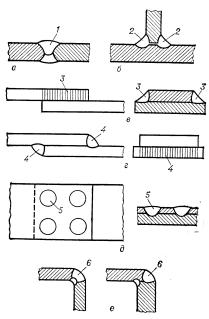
Виды сварных соединений и типы швов при дуговой сварке : a — стыковое; 6 — тавровое; e , z, ∂ — нахлёсточные; e — угловое; 1 — стыковой шов; 2 — угловой шов таврового соединения; 3 — фланговый угловой шов нахлёсточного соединения; 4 — лобовой угловой шов нахлёсточного соединения; 5 — электрозаклёсточный шов нахлёсточного соединения; 6 — шов углового соединения.
